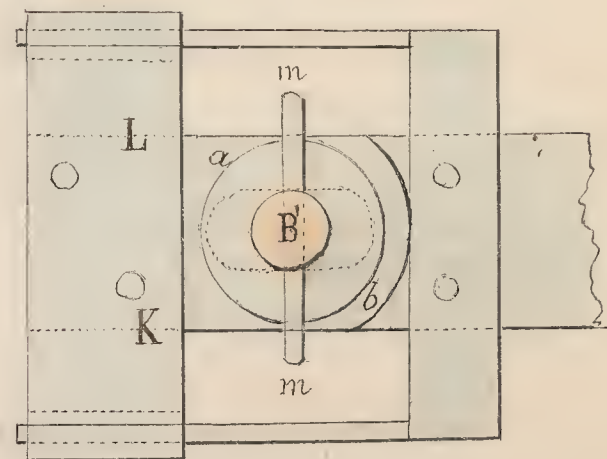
Assemblage des Cambestria et des Pivots avec la Fourche du Toit.
